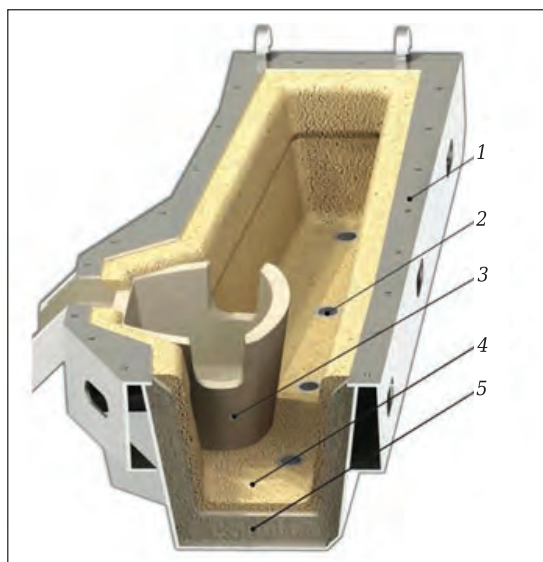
Промежуточный ковш МНЛЗ: 1 — кошуа промежуточного ковша; 2 — стакан-дозатор; 3 — металлоприемник; 4 — торкрет-слой; 5 — рабочий слой
